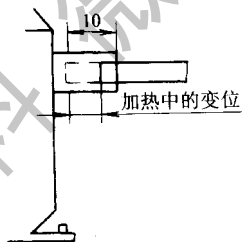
压缩机导管与制冷剂管的焊接结构
